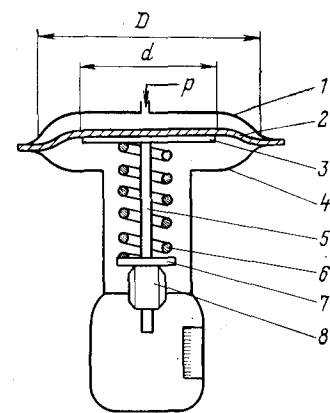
Мембранно-пружинный пневматический исполнительный механизм
